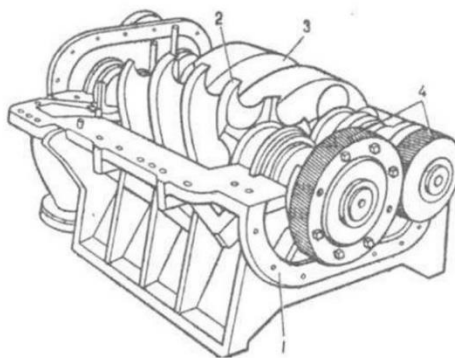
Винтовой компрессор: 1-корпус; 2,3-ведущий и ведомый винтовые роторы; 4-шестерни
